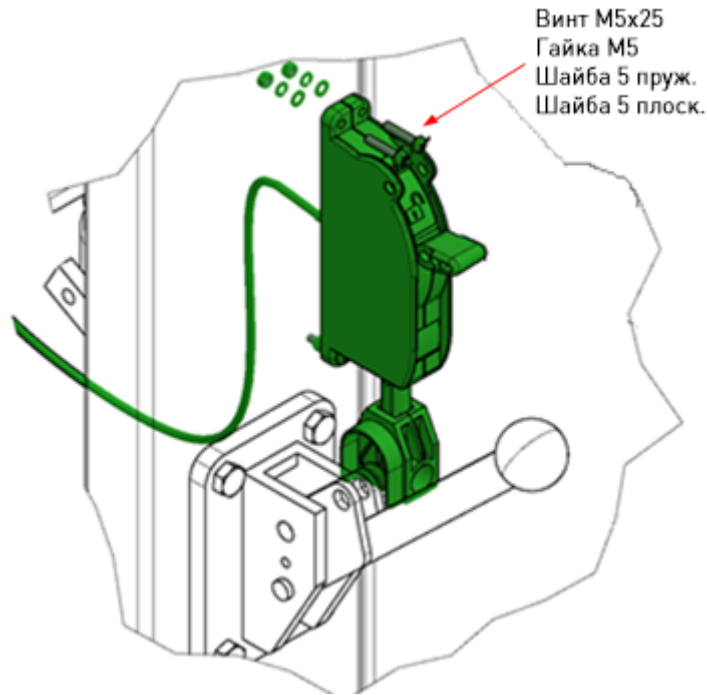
Установка блокиратора с разнесенными разъединителями
